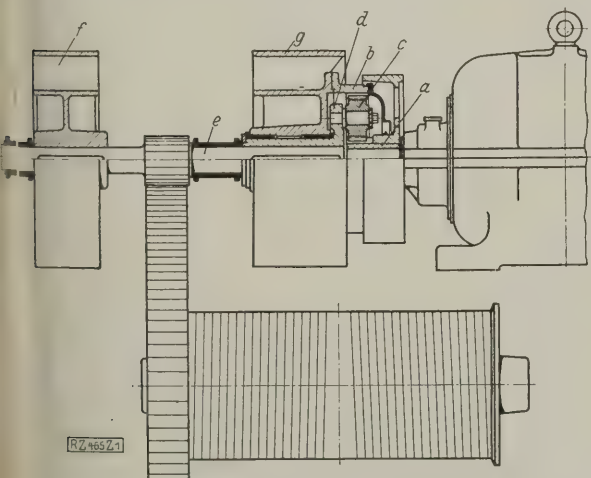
Ausgleichgetriebe in Stirnradausführung
